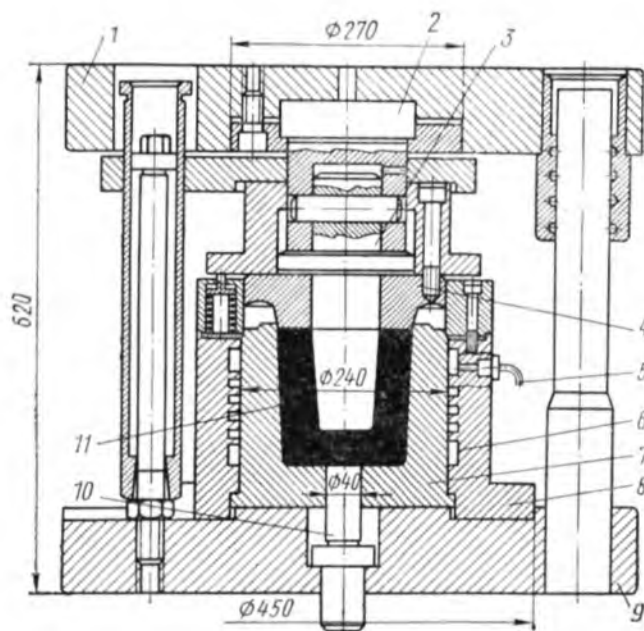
Штамп для жидкой штамповки полой поковки:
